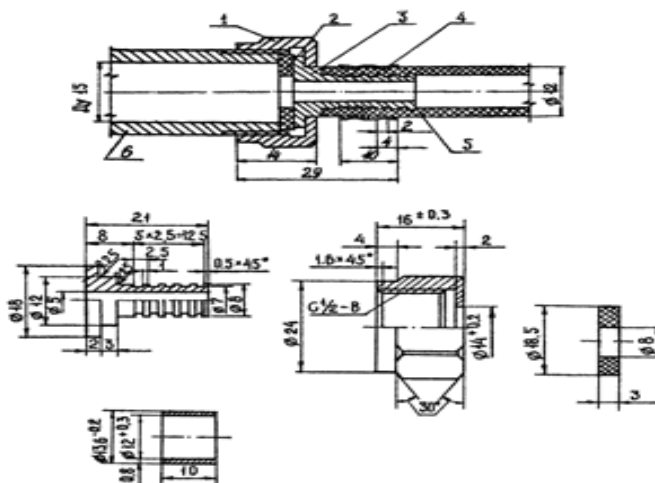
Конструкция полиэтиленовой подводки с ниппельными соединительными узлами:
